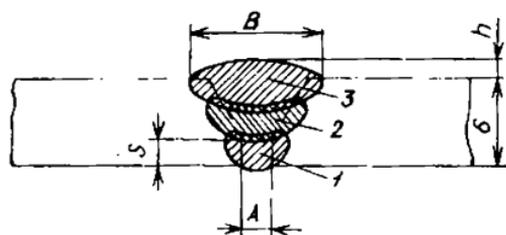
Последовательность наложения слоев сварного шва
